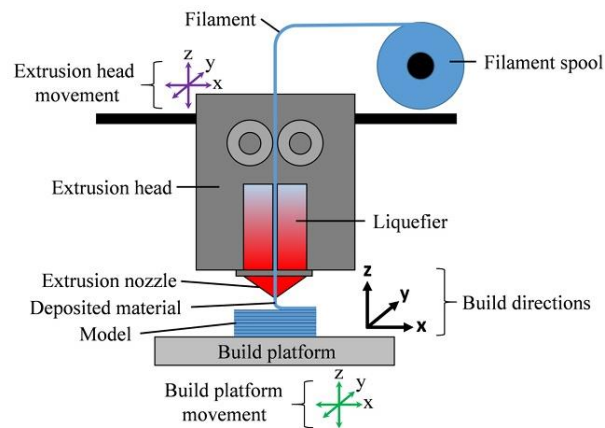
Componentes e estrutura básica de equipamentos de impressão 3D do tipo FDM [20]
